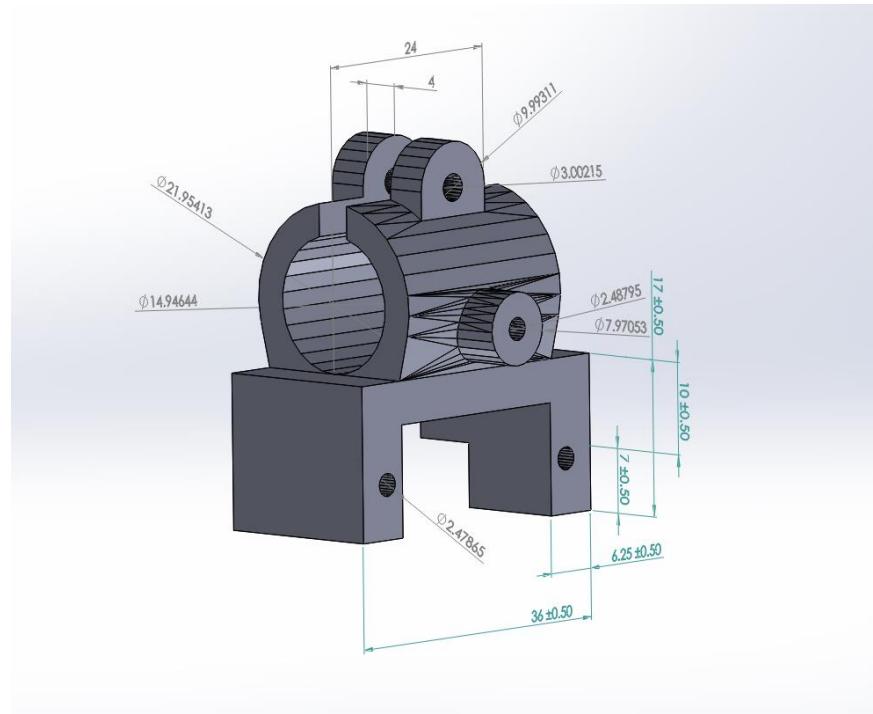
C: Modelado en 3D del bloque de rodamiento lineal.
